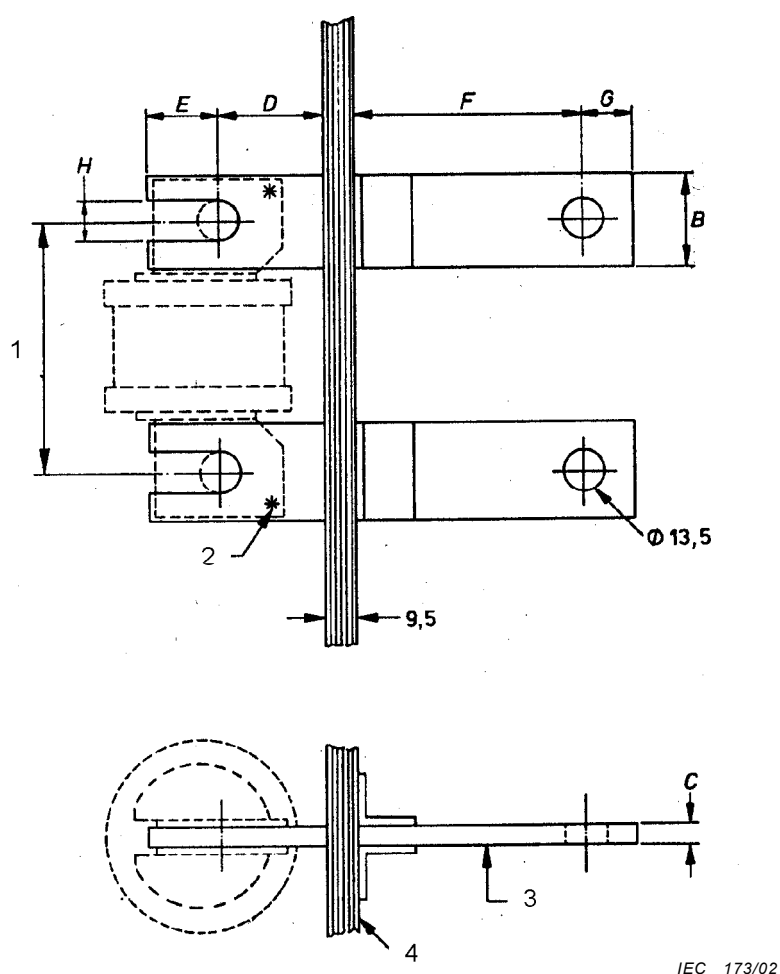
(VI) – Dimensions pour les éléments de remplacement
